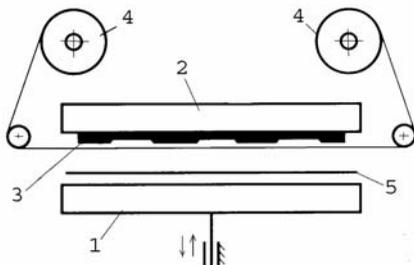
Тигельный позолотный пресс: 1 — нижняя подвижная плита (стол) с талером; 2 — верхняя плита (тигель) с электронагревательным элементом; 3 — штамп; 4 — фольговое устройство (аппарат); 5 — лист
